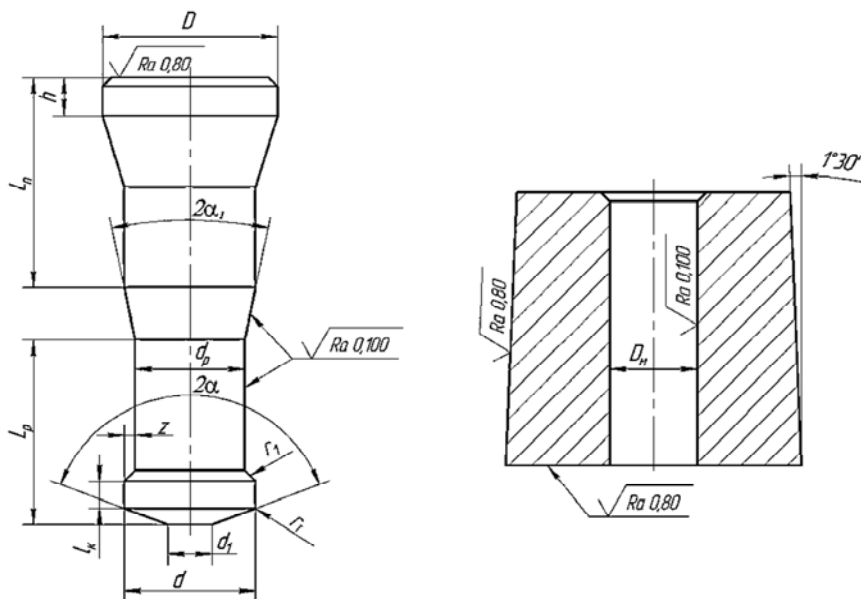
Типовые конструкции пуансона и матрицы для обратного выдавливания
